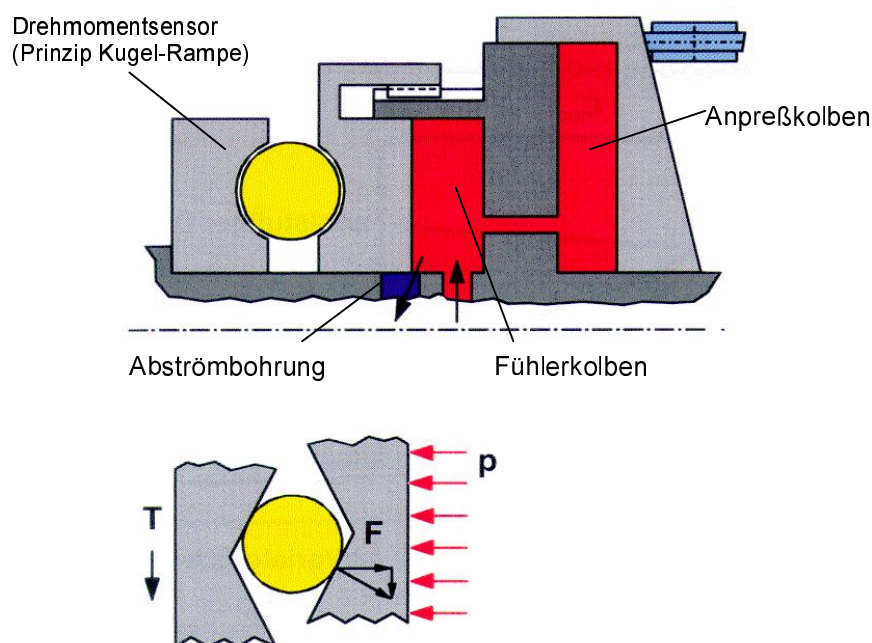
Hydraulische Steuerung des Prototypgetriebes (LuK Doppelkolben)
